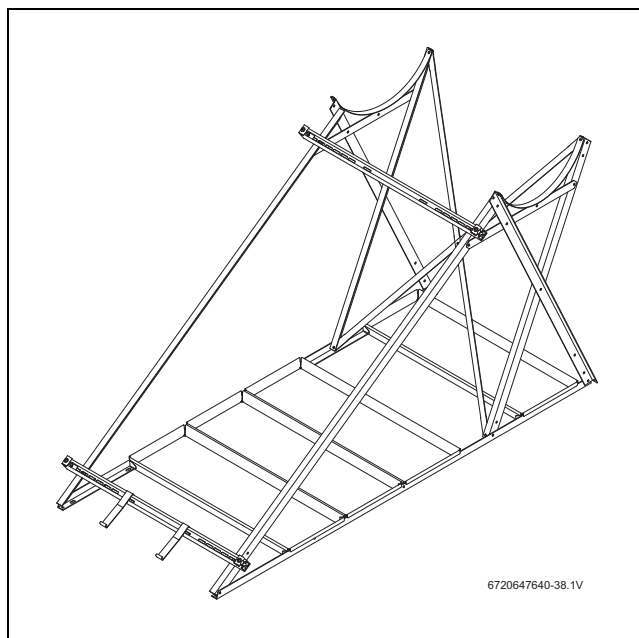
Soporte para tejado plano fija con placas de hormigón, medidas en mm (sistema de 150/200 l)
